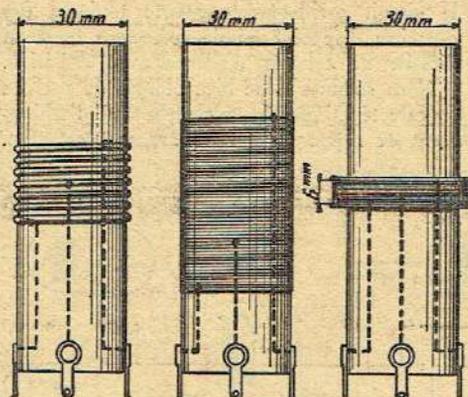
Aspect général des bobinages de l'hétérodyne modulée. A gauche : bobinage OC. — Au milieu : bobinage PO. — A droite : bobinage GO.
